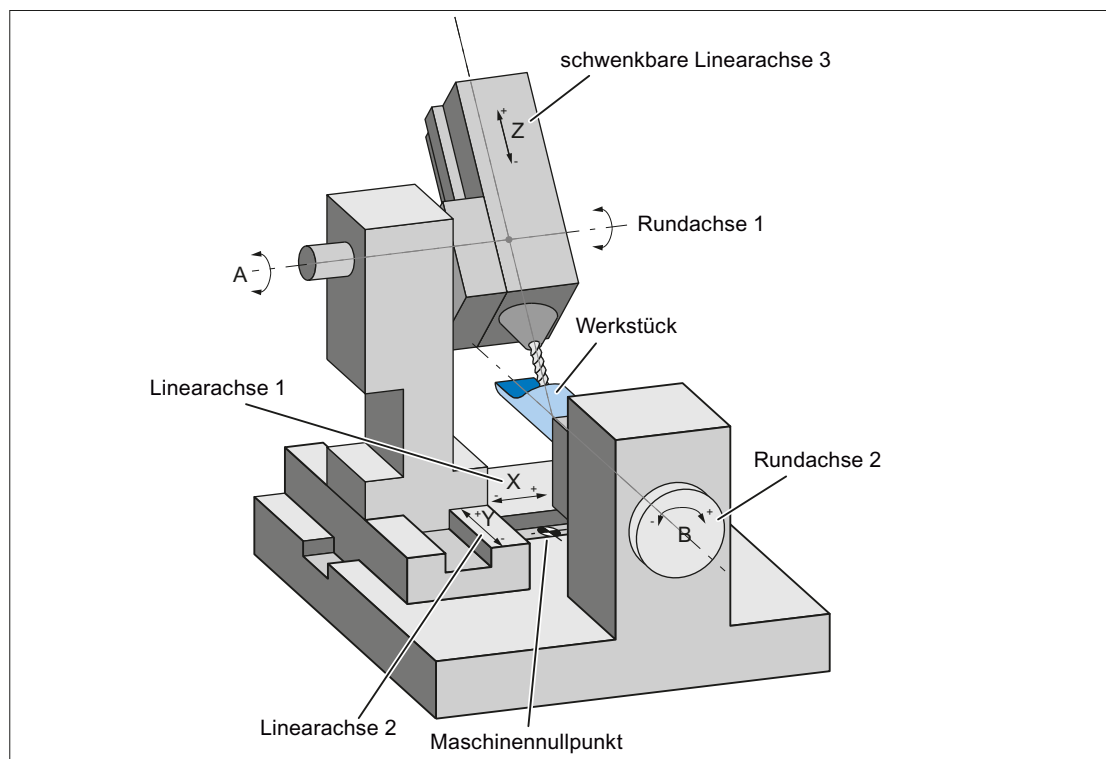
Beispiel: Maschine mit schwenkbarer Linearachse Z
